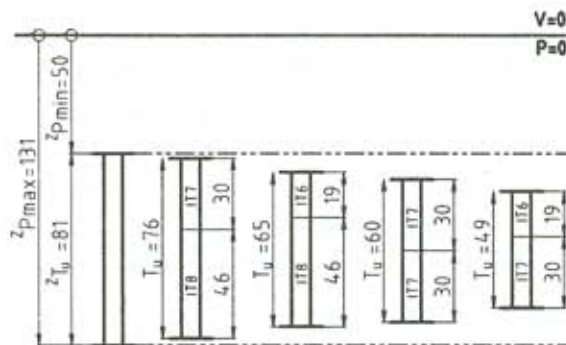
Polohy tolerančních polí - výběr ze soustavy tolerancí a uložení ISO
